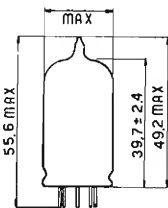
Dimensioni di ingombro della valvola 6AV6.
